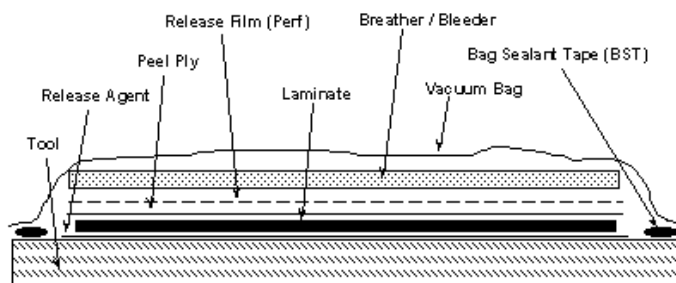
Representação de uma configuração do processo de moldagem à vácuo [About.com Composites / Plastics].
